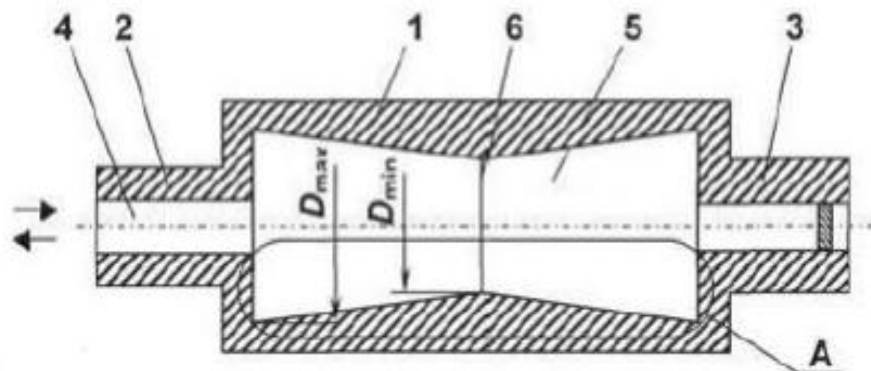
Поздовжній розріз валка: 1 – Корпус циліндра, 2,3 – цапфи, 4 – центральний канал, 5 – порожнина, 6 – менша основа
